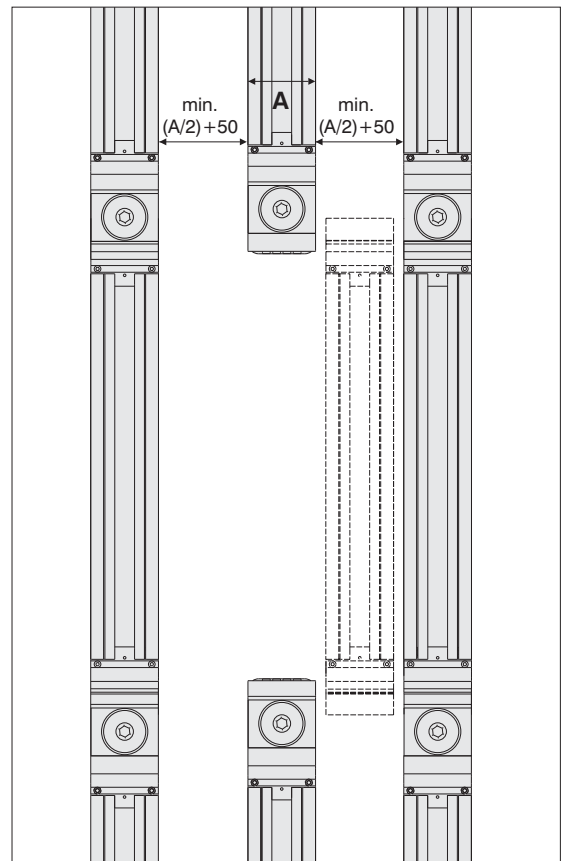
PASO POR VIGAS EN POSICIÓN PLANA
